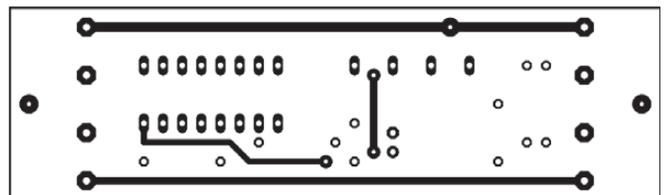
Leitungsführung auf der Platinenunterseite; Maßstab 1:1
